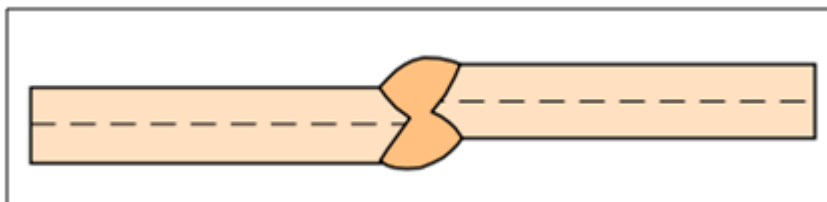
Esquema de junta soldada com desalinhamento.
